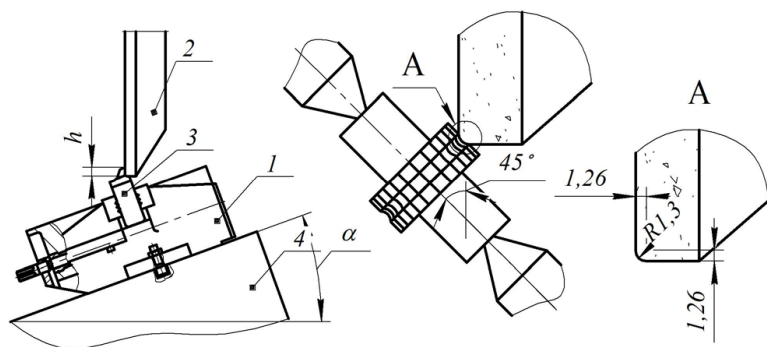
Схема заточки зубьев плоской сборной протяжки: 1 – тиски; 2 – шлифовальный круг; 3 – заготовка; 4 – стол станка
